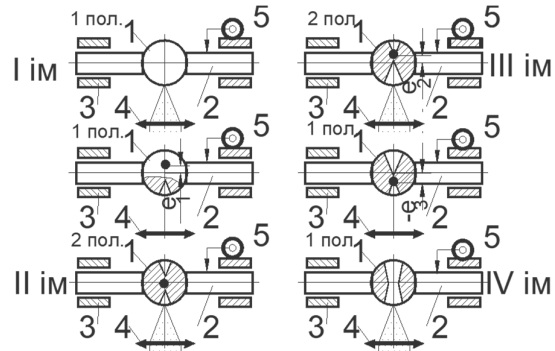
Схема реалізації операції обробки отворів циліндричної форми з почерговим опромінюванням з двох сторін, (1 – заготовка (кулька), 2 – цапфа, 3 – повітряний підшипник, 4 – об'єктив, 5 – чутник руху (обертання))
